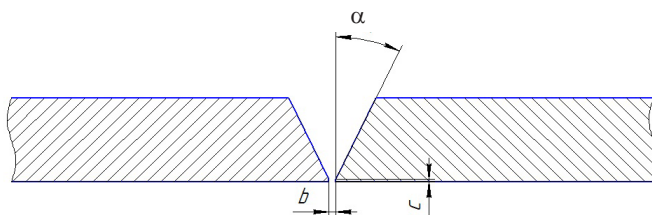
Параметры подготовки и сборки свариваемых пластин:
